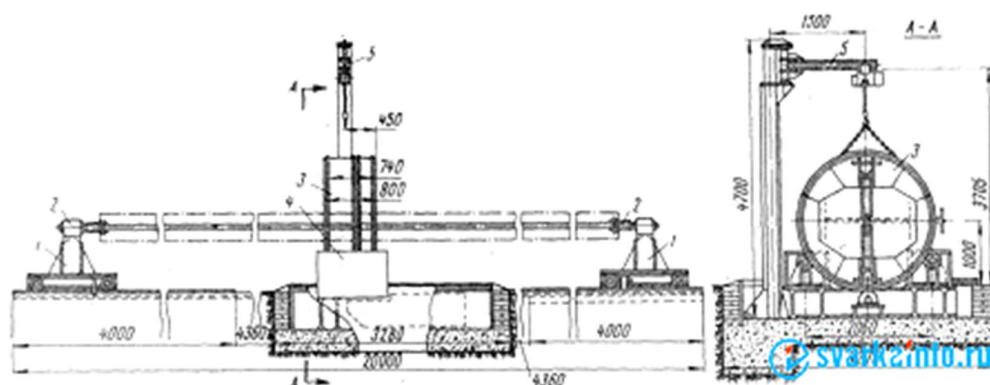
Універсальний кантувач: 1 - рухливі опори; 2 - затискачі; 3 - поворотне кільце; 4 - приводний механізм; 5 - консольний кран
